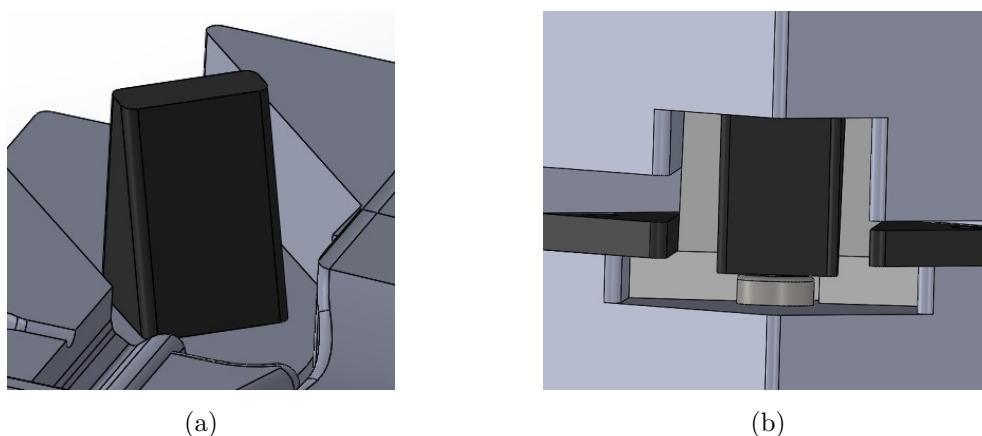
Cunha para fixação do macho, a) aspeto do cunha, b) molde fechado com cunha a fixar o macho
